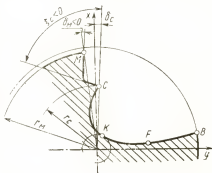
Профиль винтовой канавки сверла со стружколомом
